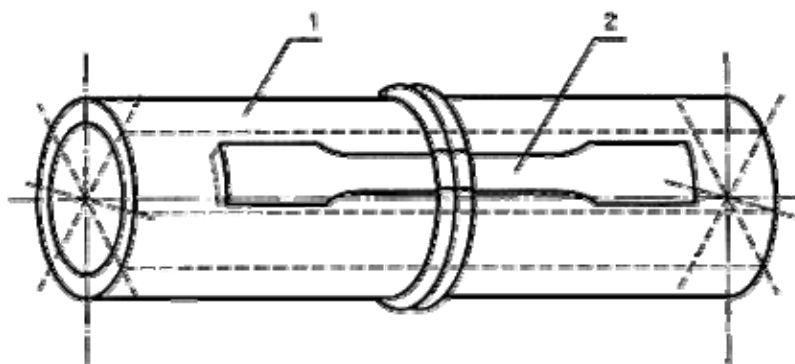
Схема вырезки образцов из сварного соединения для испытания на осевое растяжение
